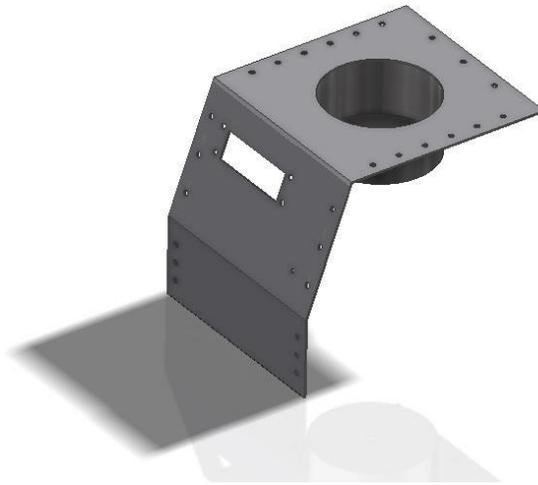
Parte superior Spin Coater con cubierta cilíndrica.
